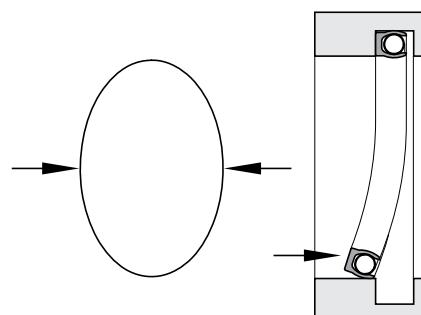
Установка закрытой посадочной канавки в режиме штока
